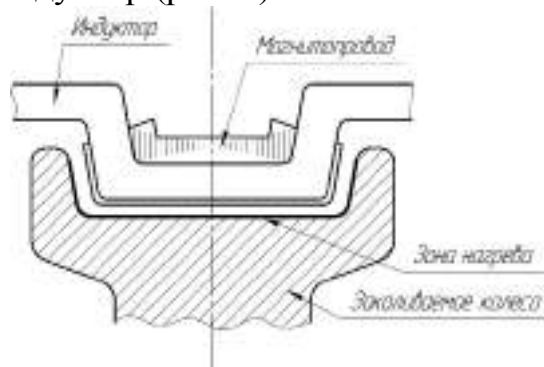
Конструктивная схема участка колеса с индуктором (разрез)
